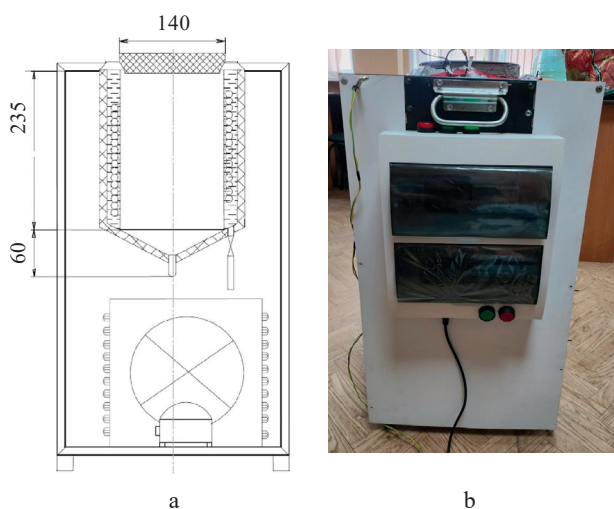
Конструкция криоконцентратора: а – схема устройства; б – внешний вид
